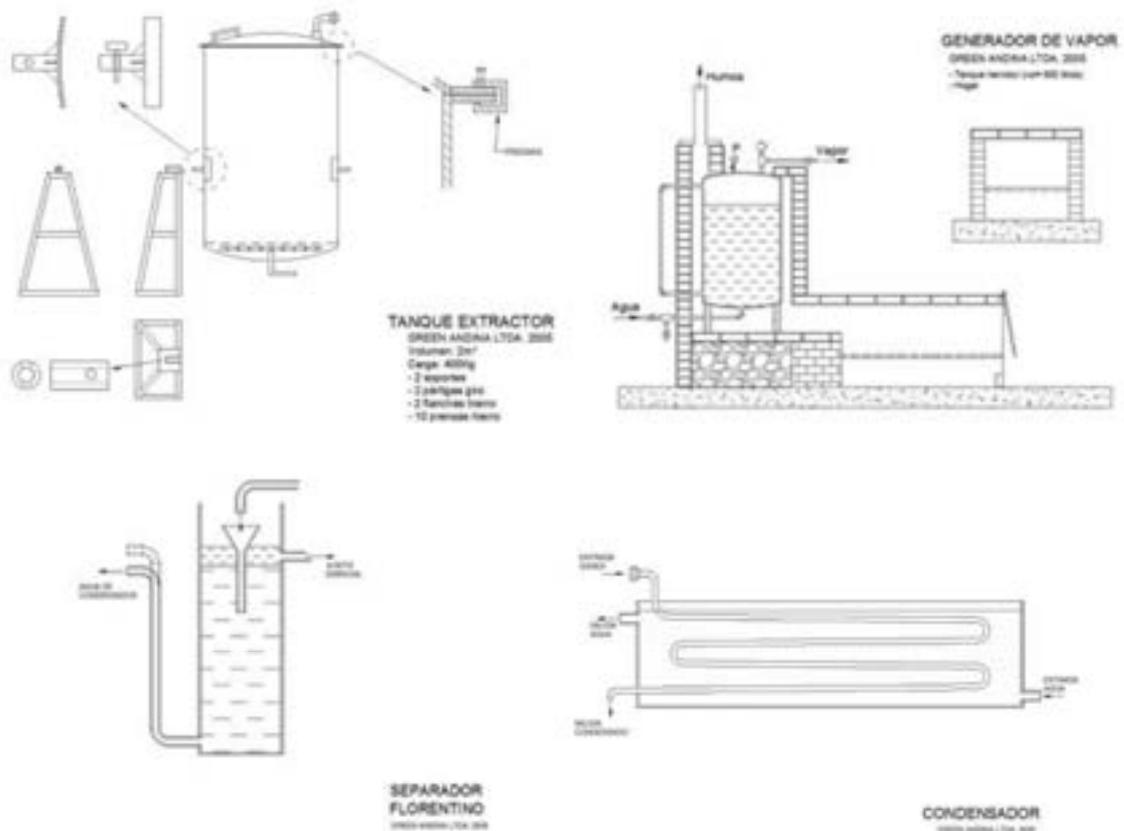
30. Planta de Extracción. Esquimos.
